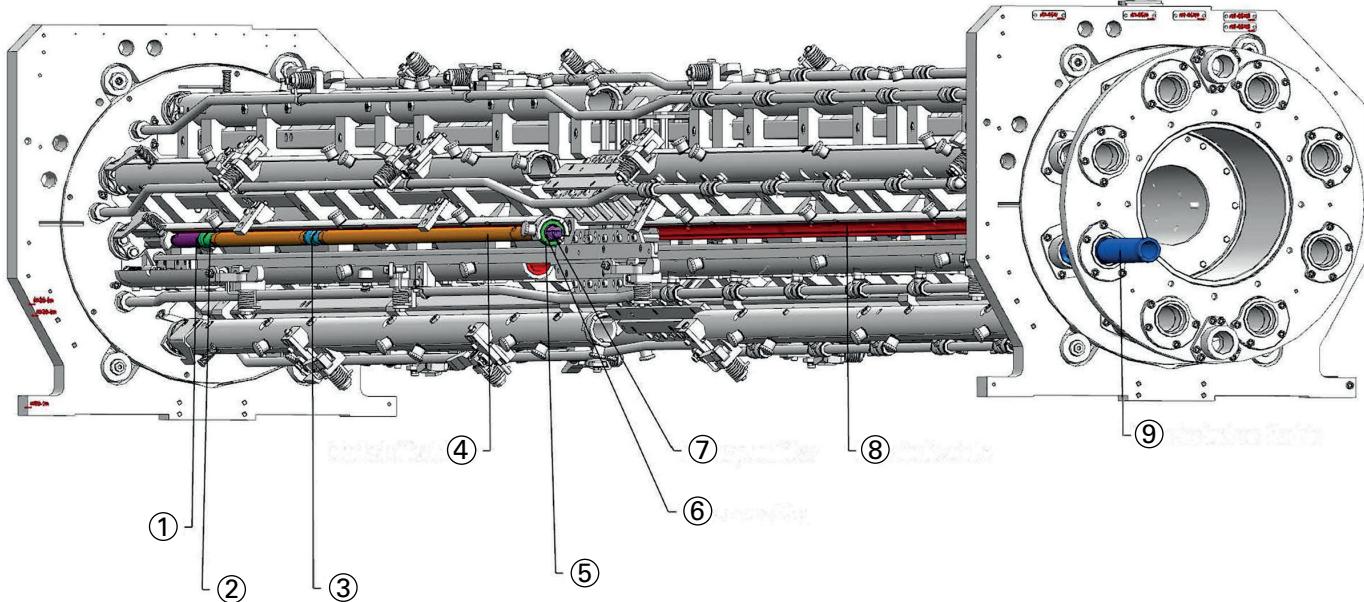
3300 (Beispielbild für die Anordnung der Wechselteile)
